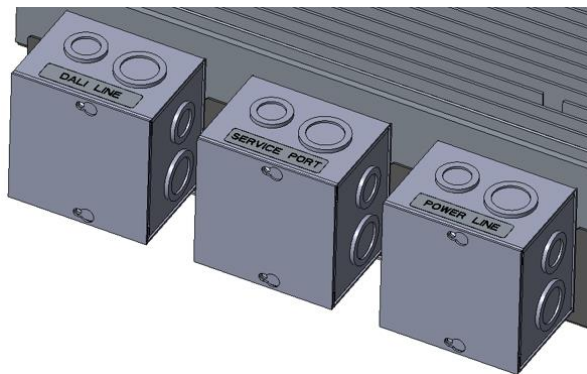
Arrière du projecteur 74-00062-01/74-00063-01
